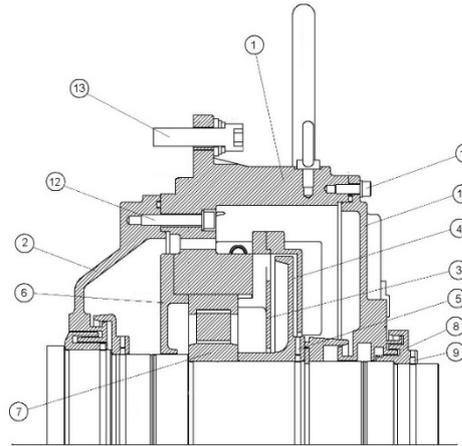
Компоненты подшипника с масляной смазкой
